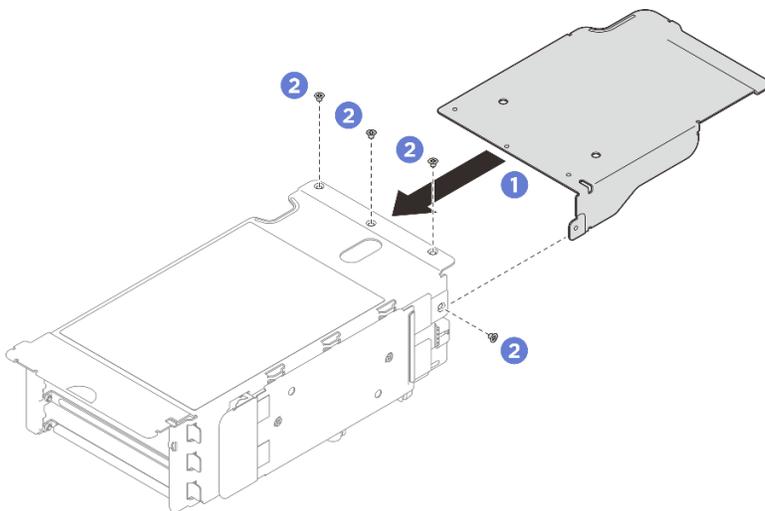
Установка расширителя платы-адаптера Riser PCIe
